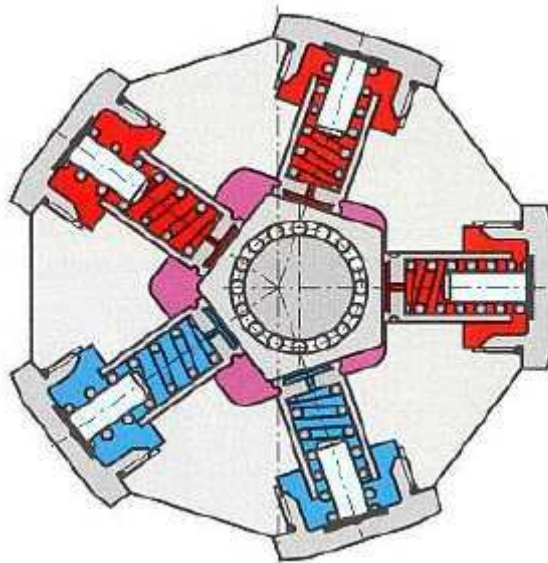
Radiální pístové čerpadlo s křivkovou oběžnou drahou[5]
